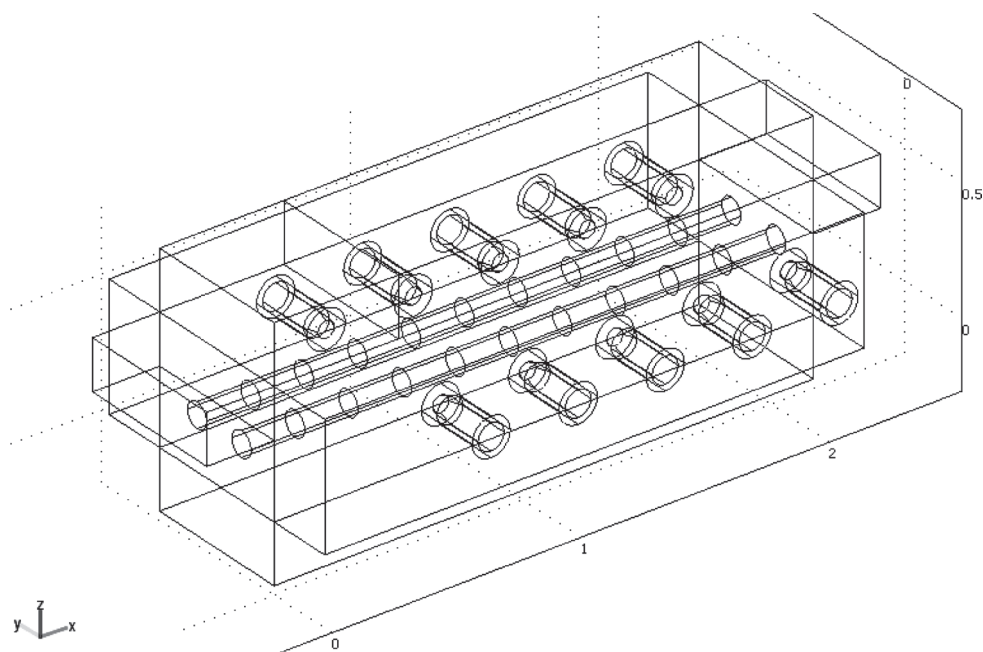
Трехмерный вид нагревательной печи скоростного струйного нагрева металла
